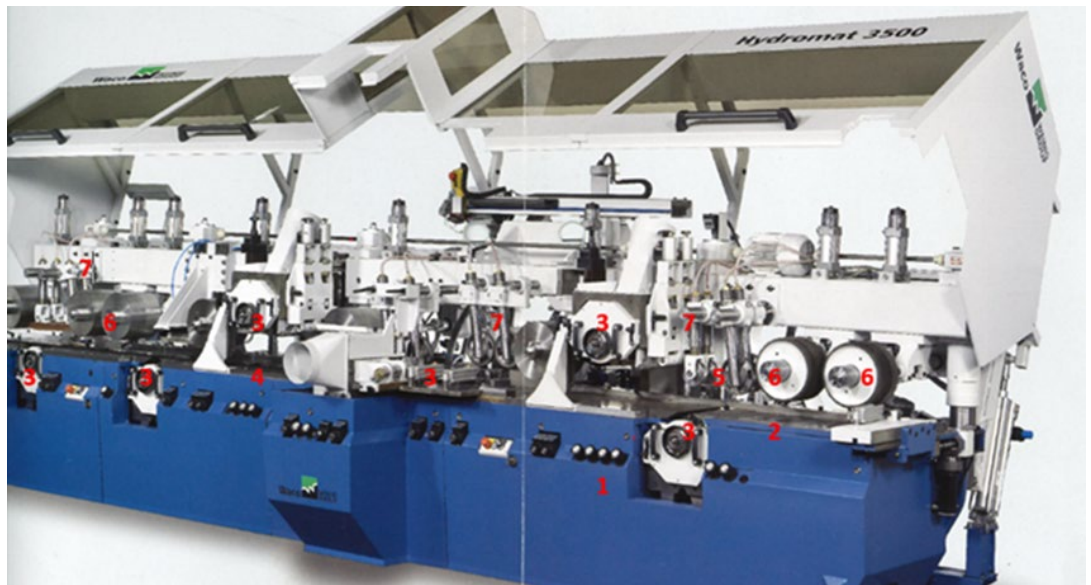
Corroyeuse-moulurière avec neuf broches, entrée des pièces à usiner à droite (source: Weinig)
